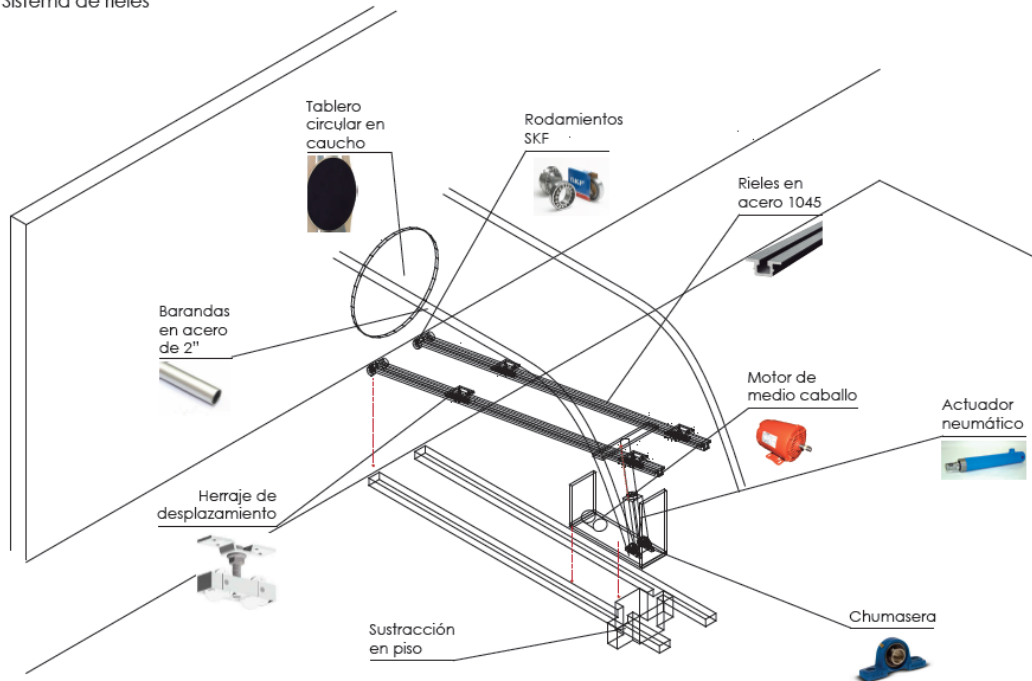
Detalle constructivo sistema de rieles. Autoría propia.
